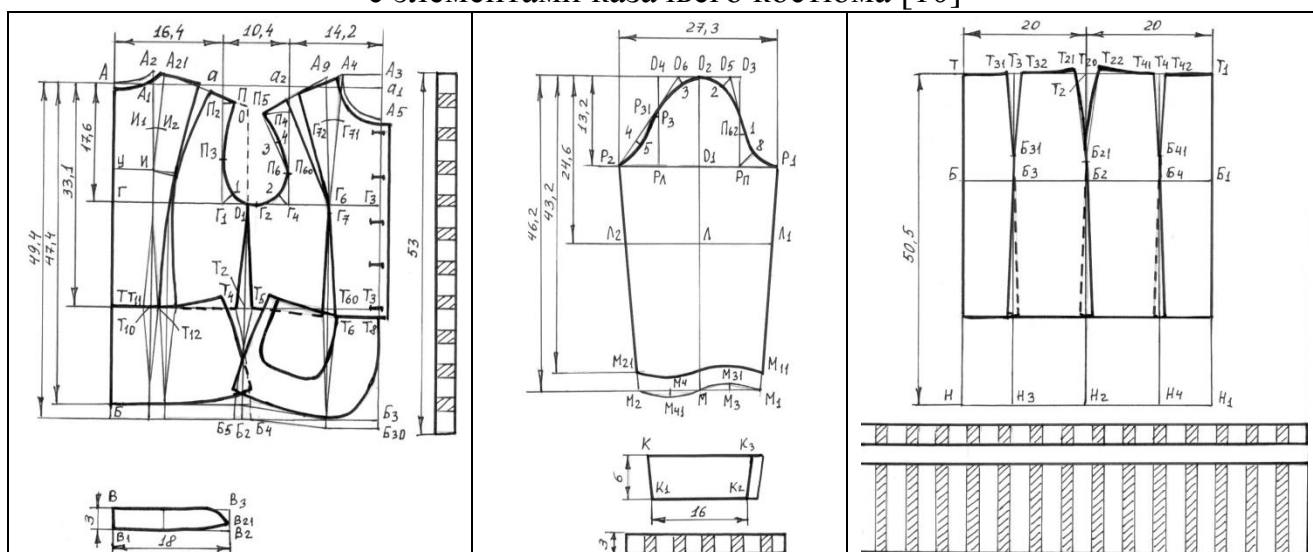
Чертёж конструкции базовой модели жакета и юбки [10]
